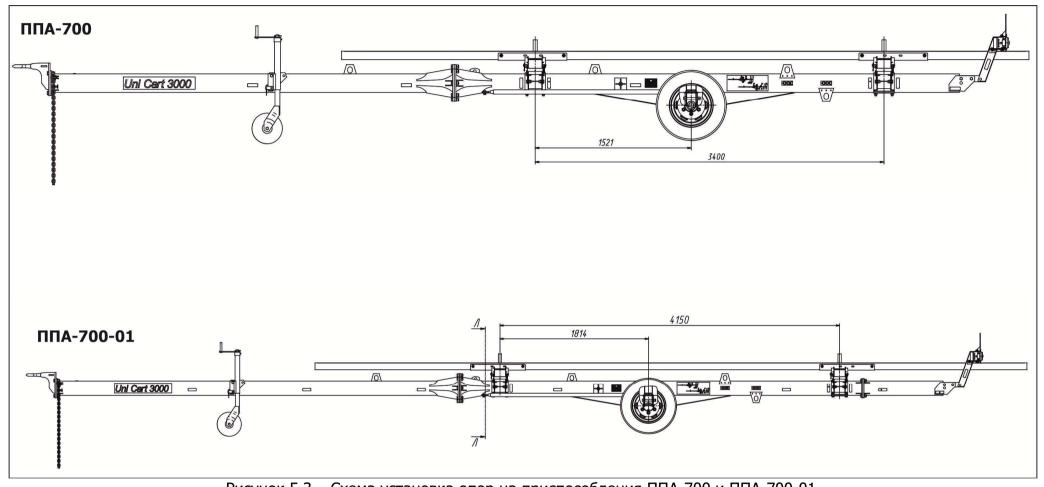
Схема установка опор на приспособления ППА-700 и ППА-700-01
